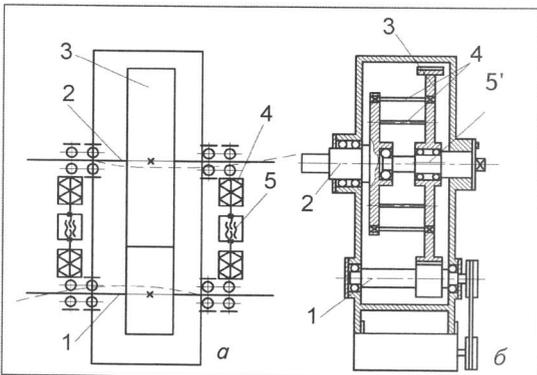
Безззорный редуктор с упругим звеном между валами в виде тарельчатых пружин (а), торсионных стержней (б): 1 и 2 — ведущий и ведомый валы, 3 — ведомое зубчатое колесо, 4 — упругое звено, 5 - регулировочный винт, 5' - эксцентриковый вал соответственно.
